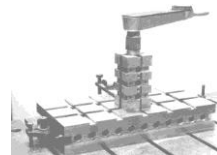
Компоновка УСП с фиксацией опоры цилиндрической шпонкой
